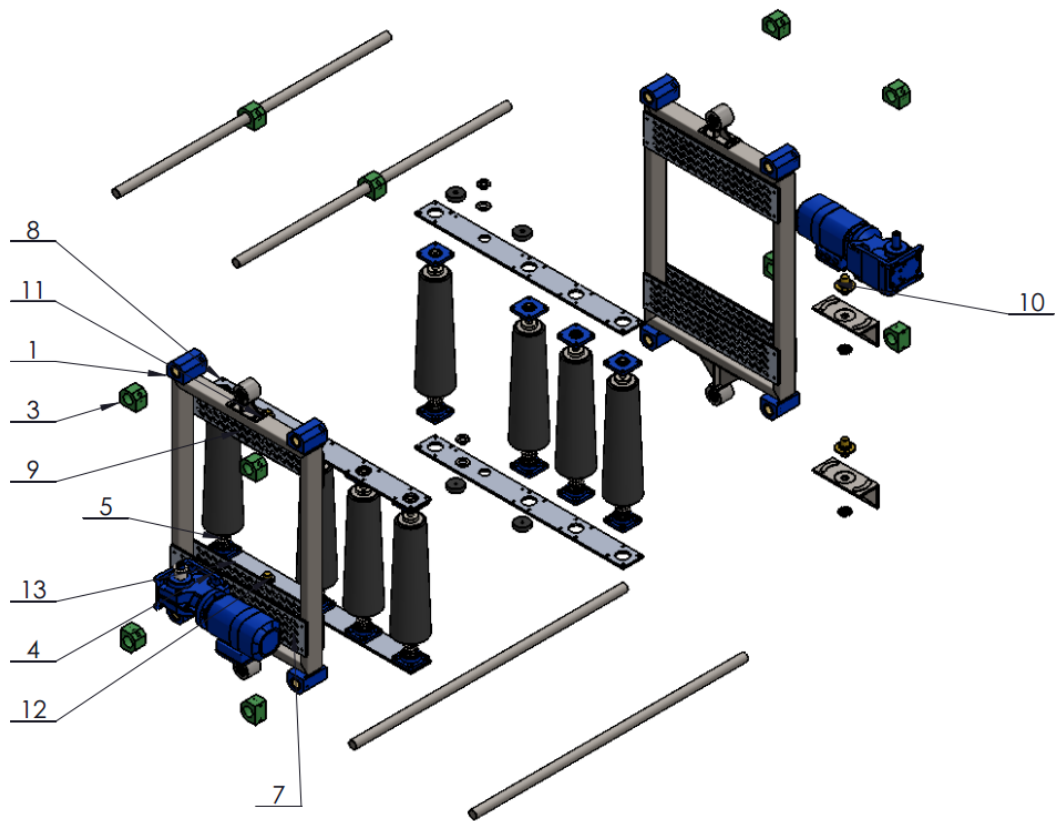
Mecanismo de arraste, representado em vista isométrica explodida e assemblada
